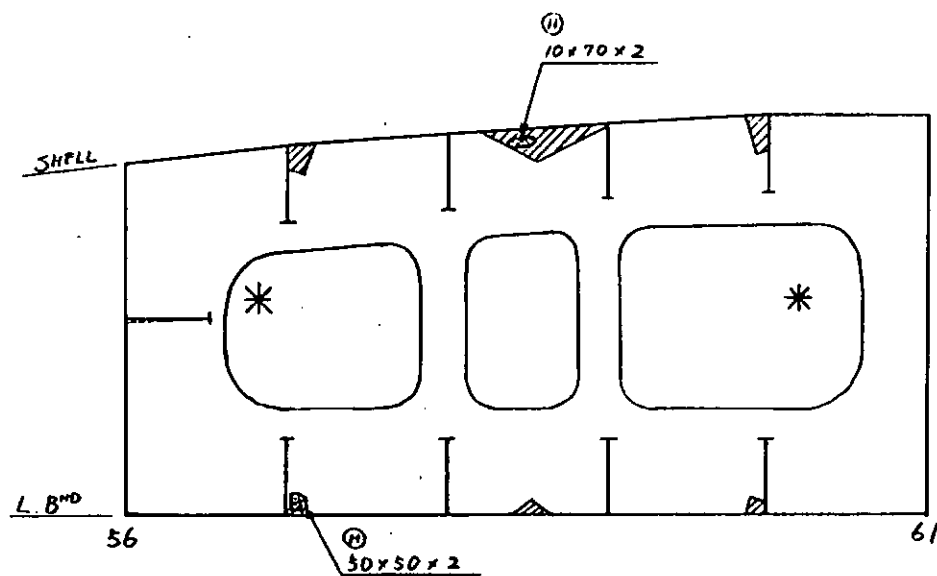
(4) №4 C.O.T(P) A TANK BOTTOM PLAN
